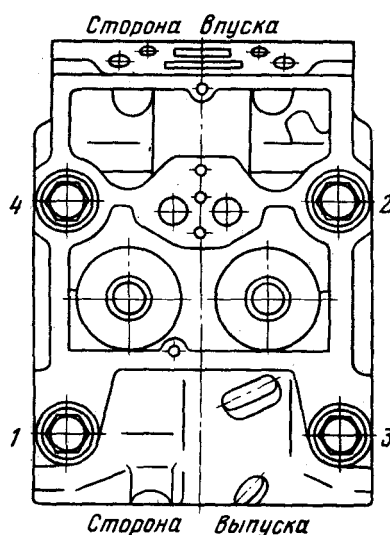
Порядок затяжки и отвинчивания болтов крепления головки цилиндров
